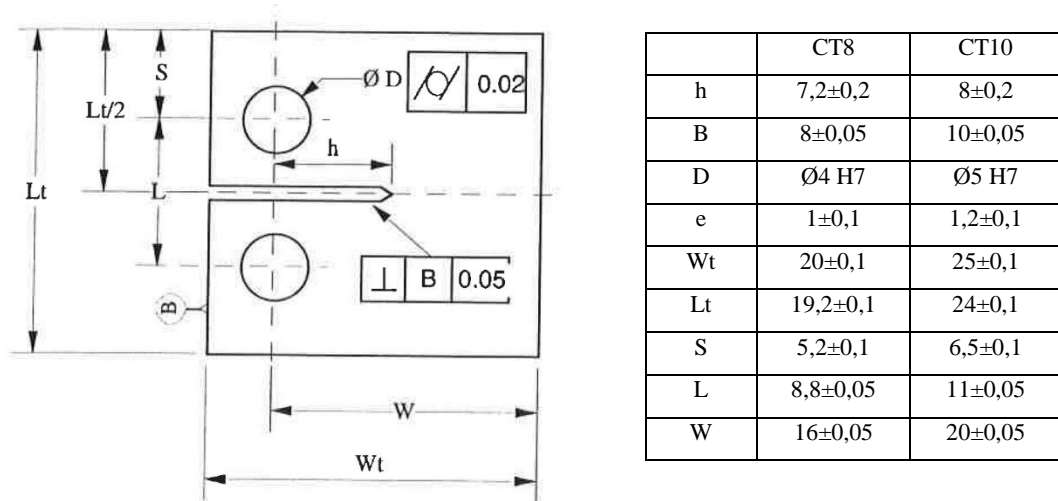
Plan d'usinage d'éprouvettes CT (dimensions données en mm)
